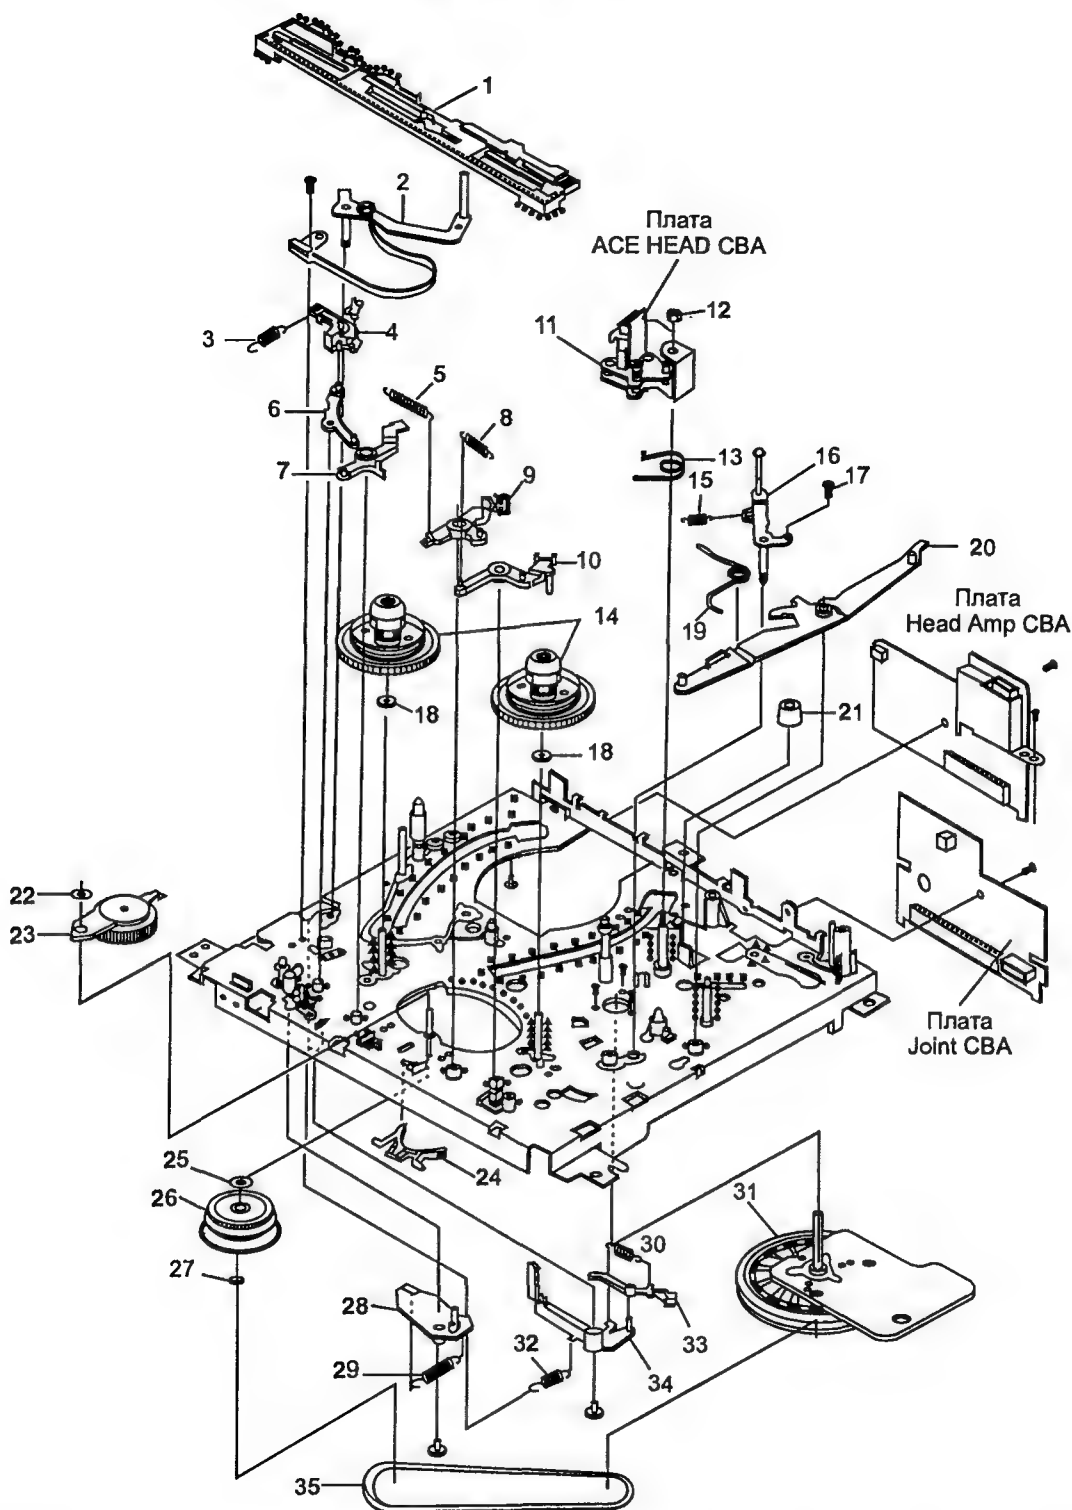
, 6. Составные части панели механизмов и головок DECK, вид 2: 1 — рычаг изменения режимов; 2 — ленточный тормоз; 3 — пружина тормоза; 4 — главный тормоз; 5 — пружина тормозного рычага; 6, 7 — тормозные рычаги; 8 — пружина тормоза; 9 — главный тормоз; 10 — тормозной рычаг; 11 — звуковая и синхронизирующая головки в сборе; 12 — шестигранная гайка М3; 13 — пружина регулятора головки; 14 — основания под катушечников; 15 — пружина рычага направляющей ленты; 16 — направляющая лента; 17 — винт регулировки рычага направляющей ленты; 18 — втулка; 19 — пружина рычага; 20 — главный рычаг; 21 — регулировочная гайка; 22 — втулка-муфта; 23 — паразитный рычаг; 24 — рычаг паразитного ролика; 25 — шайба муфты; 26 — муфта; 27 — шайба; 28 — управляющий рычаг; 29 — пружина натяжения управляющего рычага; 30 — пружина рычага записи; 31 — двигатель ВВ; 32 — пружина рычага записи; 33, 34 — рычаги записи; 35 — ремень двигателя ВВ
